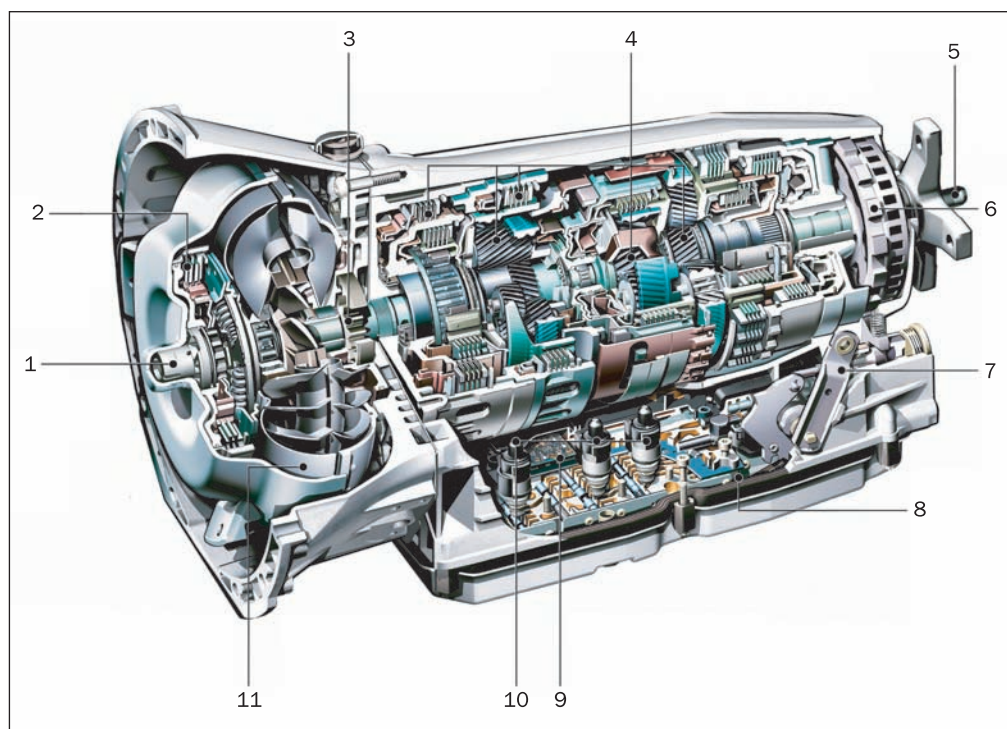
Устройство коробки передач 7G-Tronic: 1 — ведущий вал; 2 — фрикцион блокировки гидротрансформатора с гасителем крутильных колебаний; 3 — масляный насос с контролем давления; 4 — фрикционы и планетарные передачи; 5 — выходной вал; 6 — стояночный тормоз; 7 — селектор; 8 — электронный блок управления; клапаны и датчики, встроенные в поддон; 9 — электронный блок переключения передач; 10 — высокоскоростные соленоиды; 11 — гидротрансформатор
